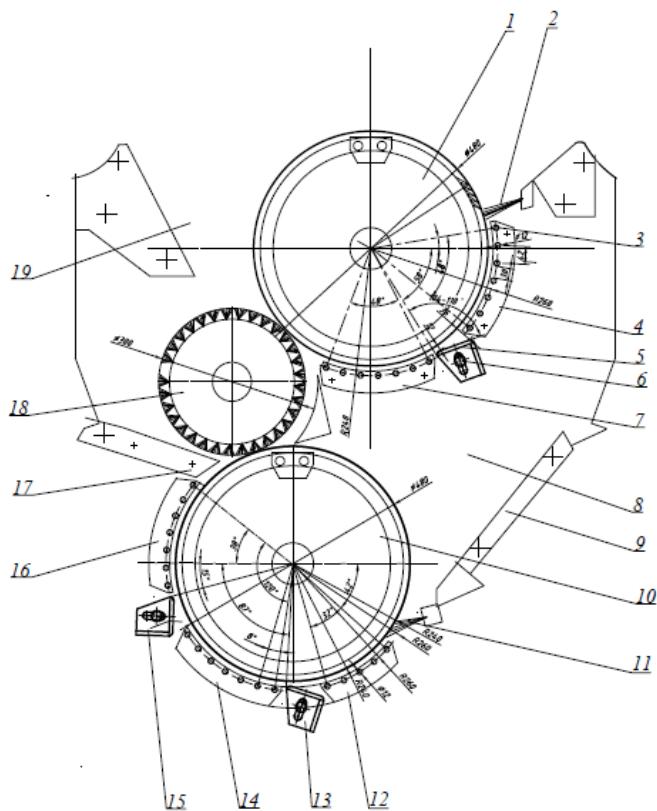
Модернизированный очистительный блок ЕН-177; 1- основной пильчатый барабан, 2,11-прижимная щётка, 3- колосник, 4,7,12,14,16- части колосниковой решётки, 5- направитель хлопка-сырца, 6,13,15 -перегородка, 8- зона выхода отходов, 9- лоток зоны выхода отходов, 10- регенерационный пильчатый барабан, 17-планка,18- съёмный щёточный барабан, 19- зона выброса хлопка.
